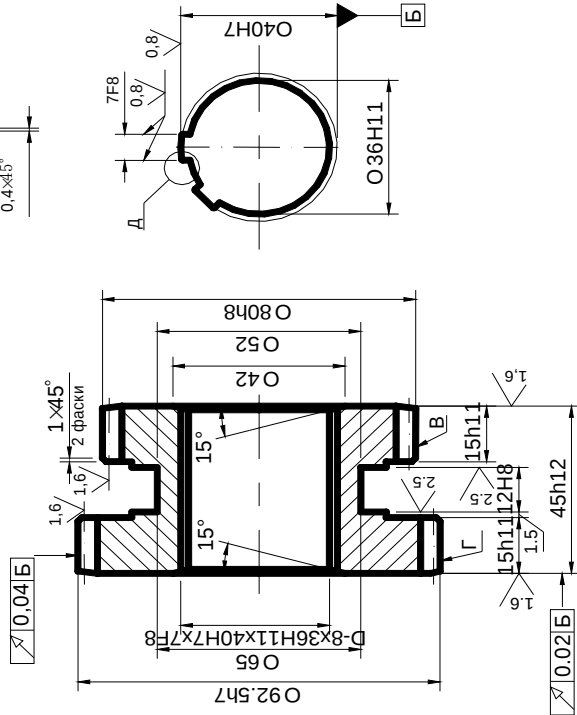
Рабочий чертеж колеса цилиндрического косозубого
